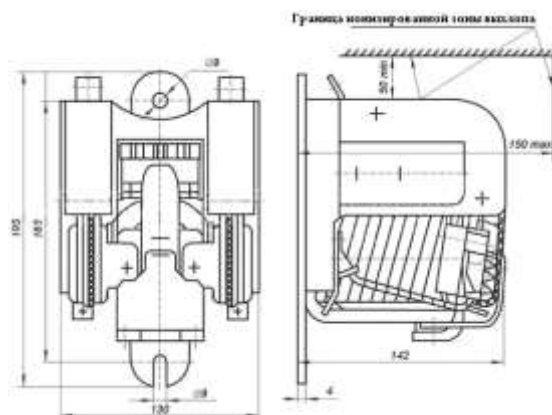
Габаритные, установочные размеры КВД-121 У2
